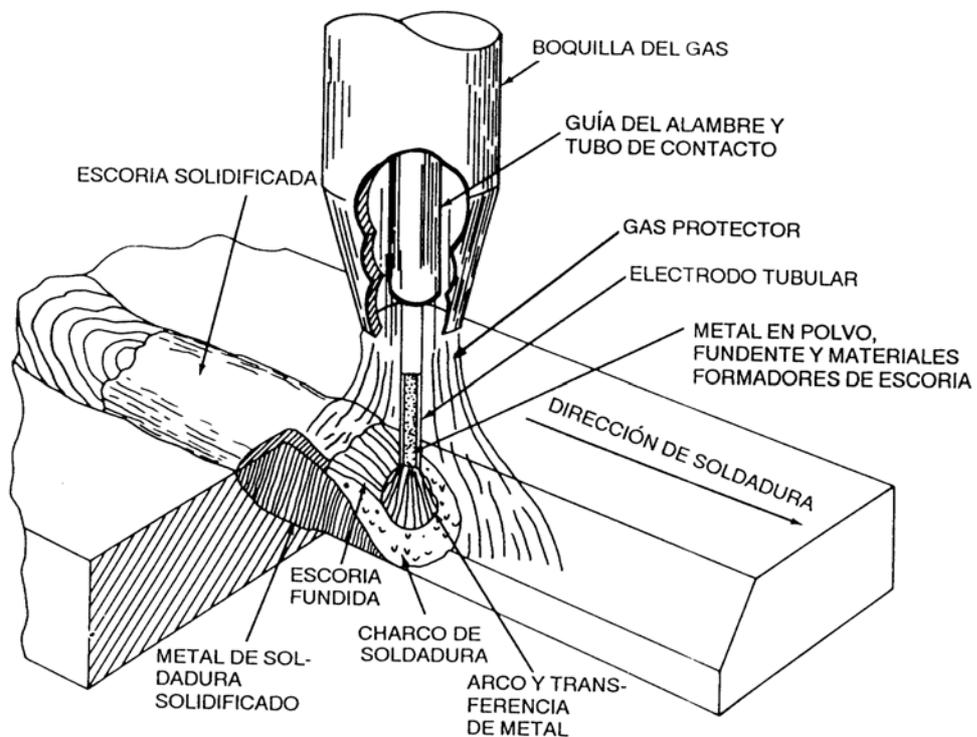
Soldadura por arco con núcleo de fundente protegida con gas
